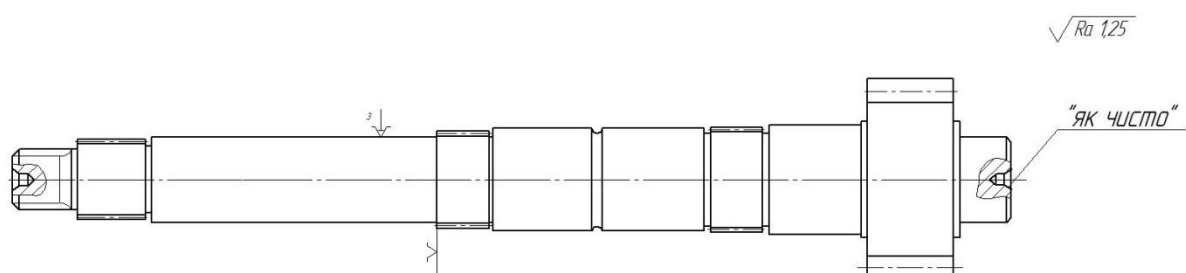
Схема базування вала під час токарної обробки центрових отворів.
